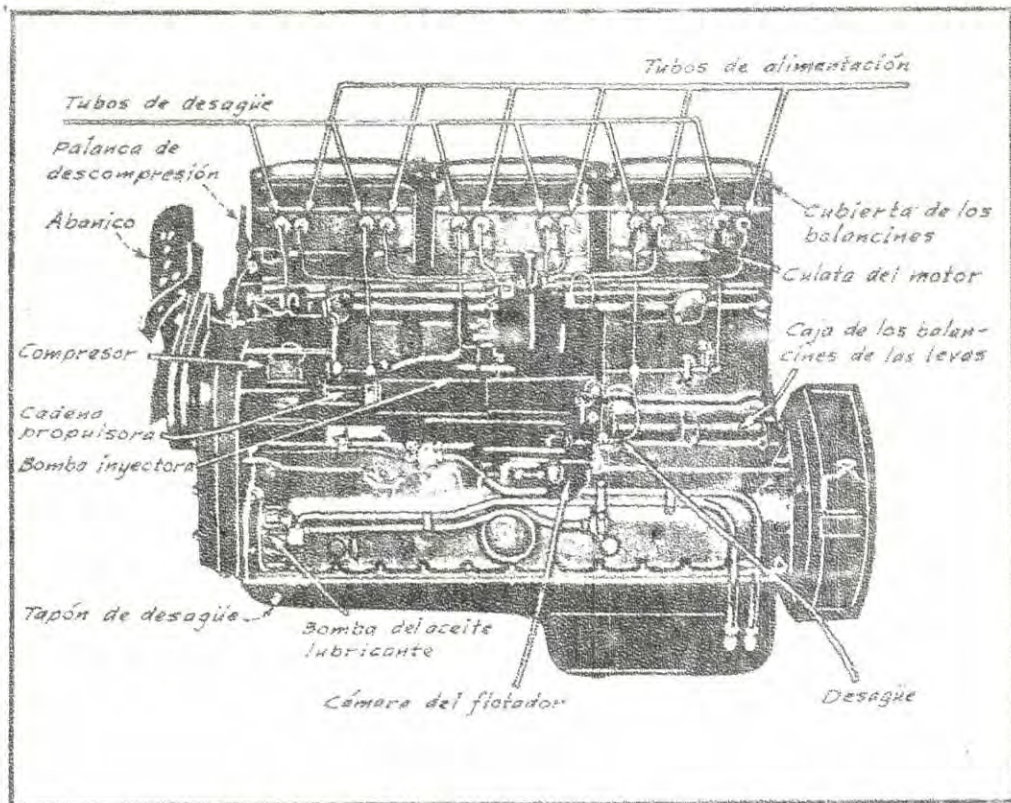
Fig. C. Motor Cummins Diesel de 6 cilindros, visto del lado de la bomba.
